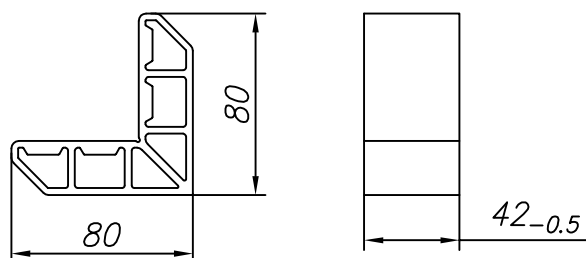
Изготовление соединителя узлового FLGU.400.0914
